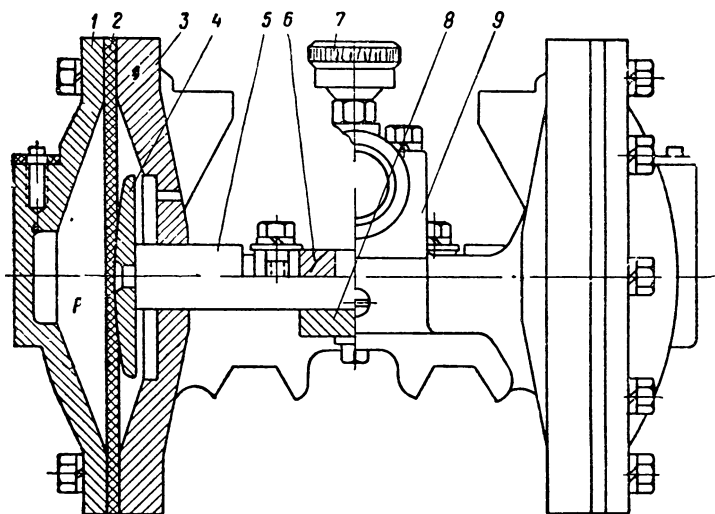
Диафрагменный привод реверсора типа ПР-1М:
